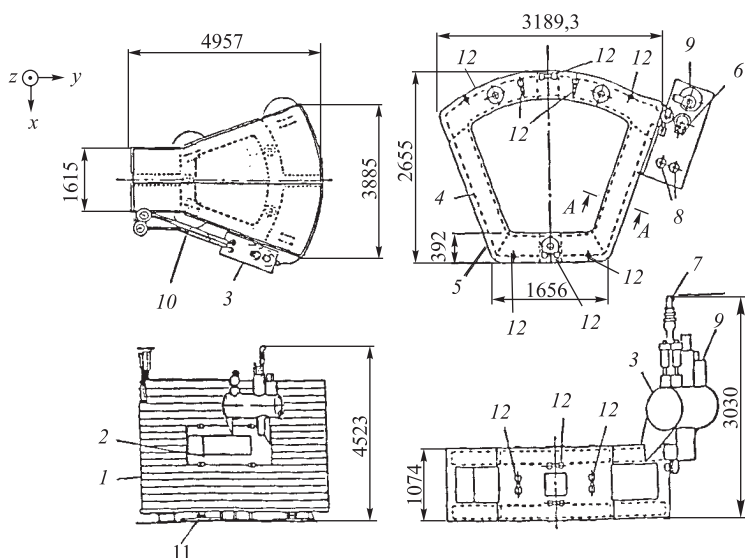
Дипольный магнит спектрометра SKS [31]: 1 — магнитопровод; 2 — криостат; 3 — гелиевый резервуар; 4 — обмотка; 5 — вакуумный кожух; 6 — токовводы; 7 — предохранительный клапан; 8 — контрольный вентиль; 9 — рефрижератор для теплового экрана; 10 — трубопроводы жидкого гелия; 11 — опоры на воздушной подушке; 12 — опоры
